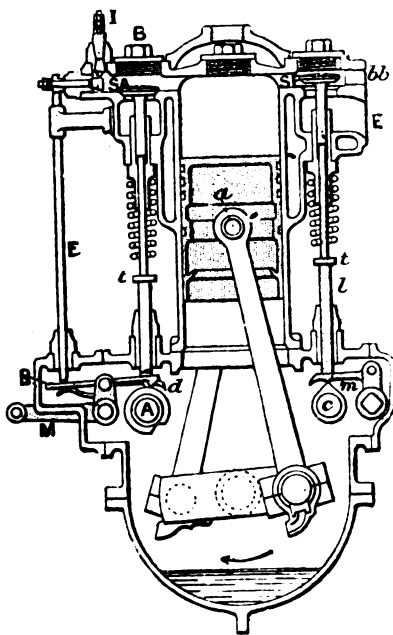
Coupe du moteur Hautier, vu de l'avant.
